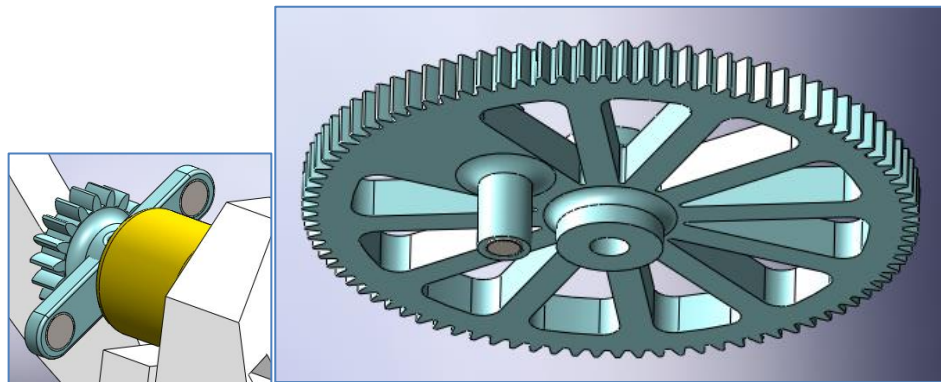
Imanes en el engranaje del motor brushless y en el engranaje que se comunica con el hombro respectivamente.
